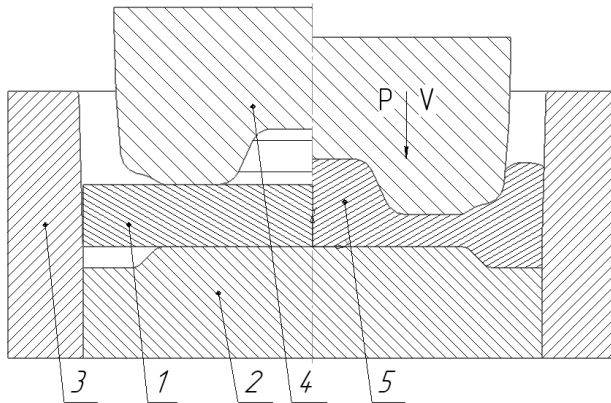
Схема процесу гарячого зворотного видавлювання напівфабрикату: 1 – заготовка; 2 – виштовхувач; 3 – матриця; 4 – пуансон; 5 – напівфабрикат
